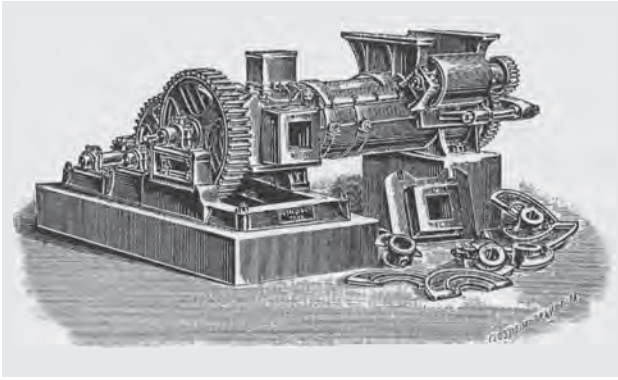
Schneckenpresse mit am Preßkopf liegendem Antrieb und seitlichem Austritt des Tonstrangs, Fa. Ed. Laeis & Co., Trier, um 1910
